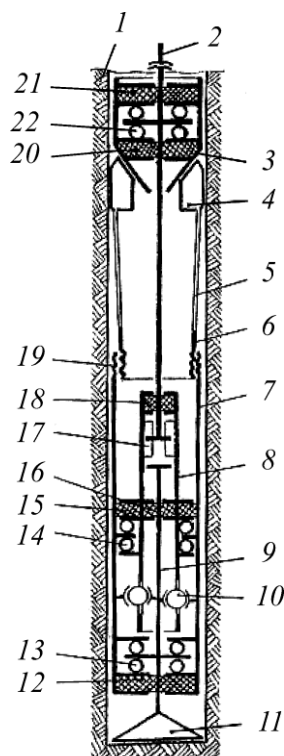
Роторно-мультипликаторный бур: 1 — скважина; 2 — бурильная труба; 3–6 — детали тормозного механизма; 7–10 — детали синусошарикового мультипликатора; 11 — алмазная коронка; 12, 15, 16, 18, 20, 21 — уплотнения; 13, 14, 22 — подшипники; 17 — шлицевое соединение; 19 — резьбовое соединение
